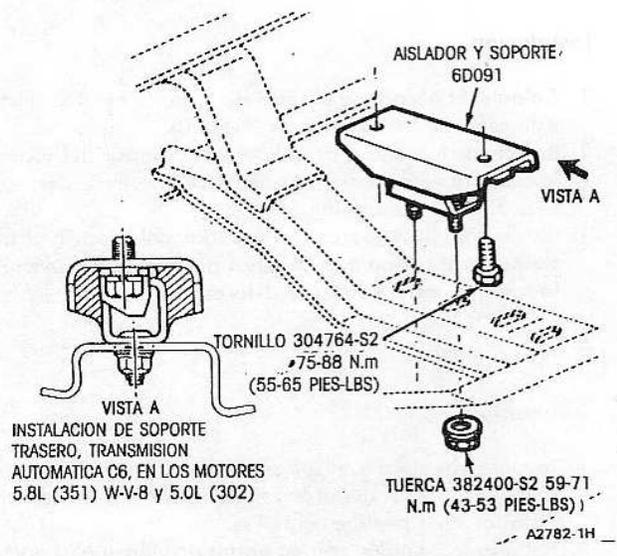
Soporte Trasero de Motor—E-100-E-250
